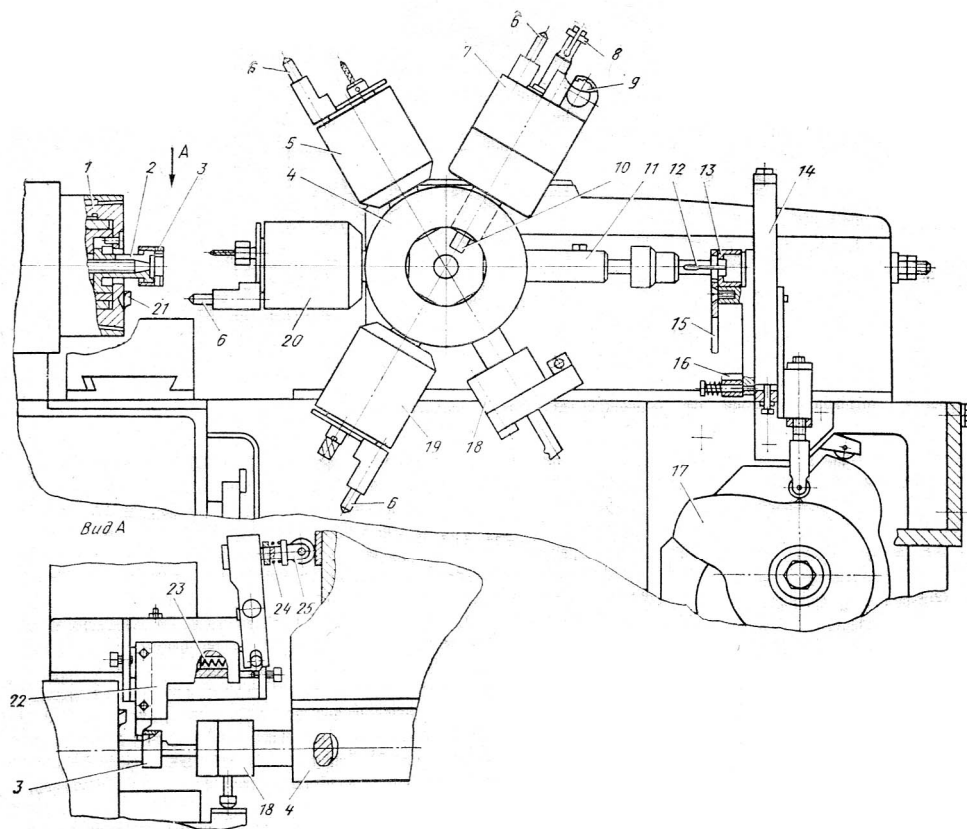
Токарно-револьверний автомат мод. 1М116, налаштований на обробку штучних заготовок
